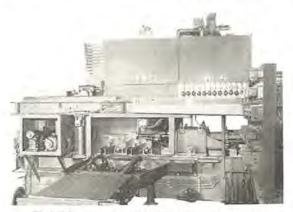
リヤアクスル 焼入装置(低 ヒズミ 機構付) Rear axle hardening machine equipped with low distorsion mechanism.
